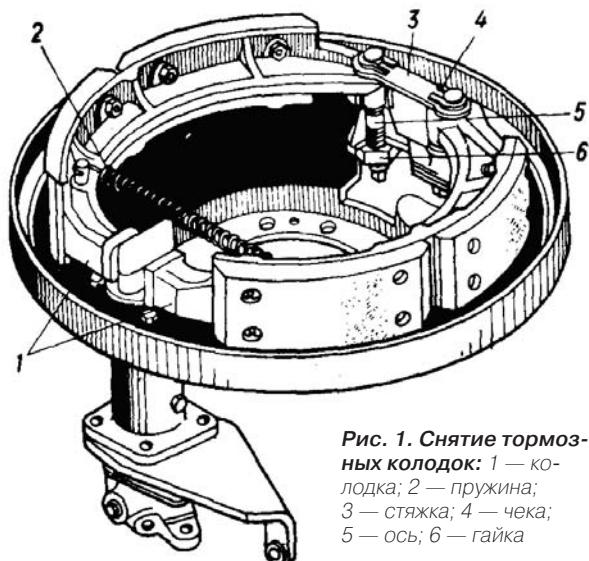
Снятие тормозных колодок: 1 — колодка; 2 — пружина; 3 — стяжка; 4 — чека; 5 — ось; 6 — гайка
